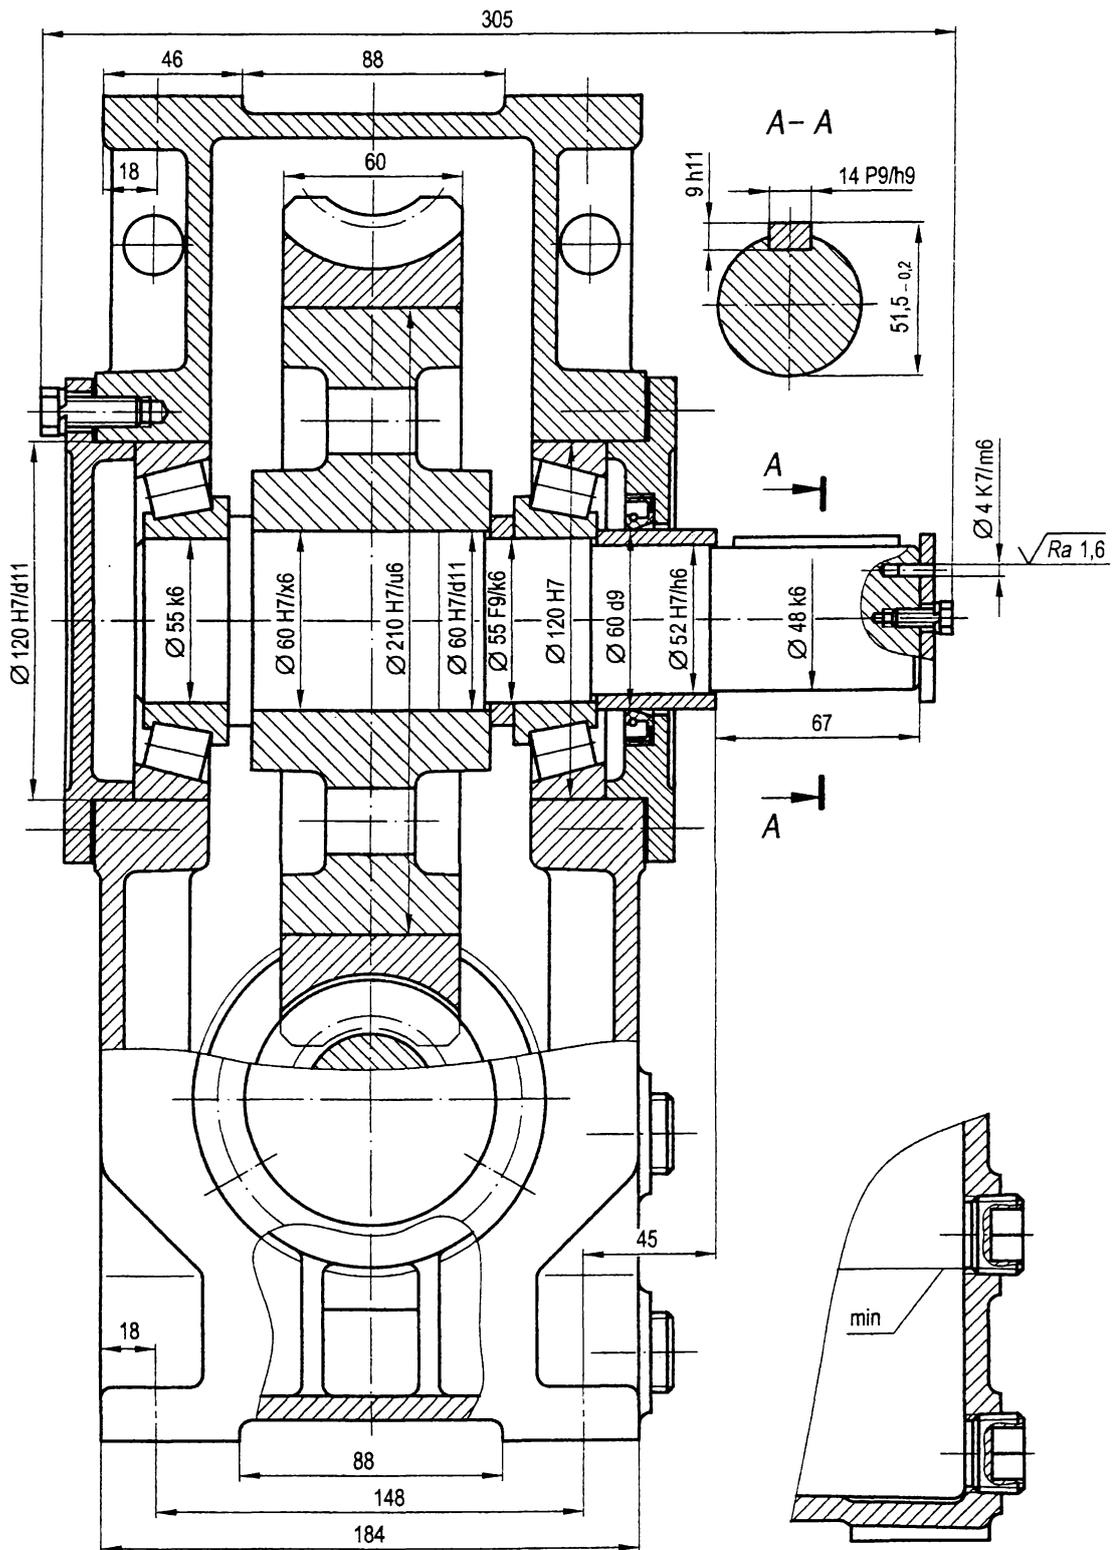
Тихоходный (выходной) вал редуктора с червячной передачей (червяк расположен горизонтально под червячным колесом)
